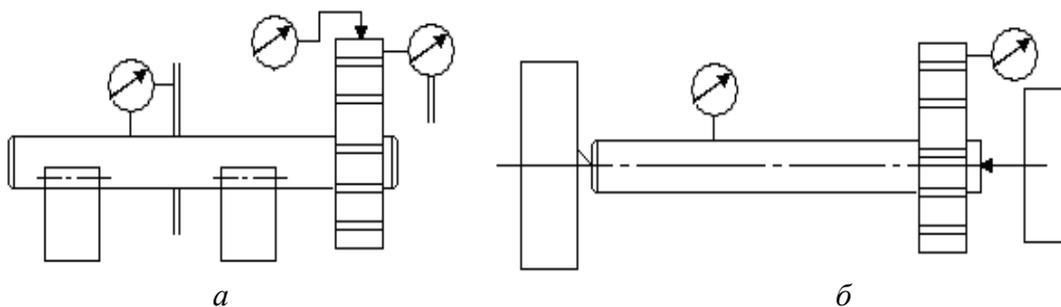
Установка зубчатого колеса для проверки на погрешность:
